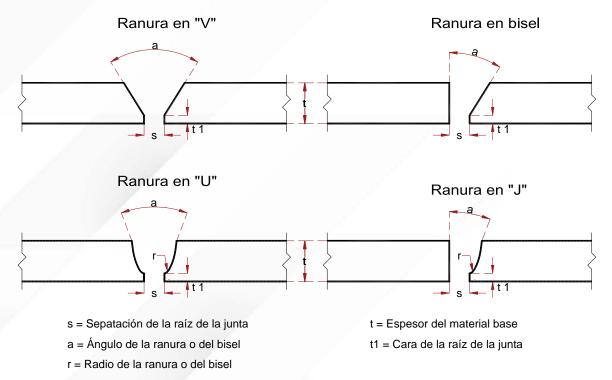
Elementos principales de las juntas (SCT, N-CTM-2\_04-001/04 Soldadura al arco eléctrico, 2004)
